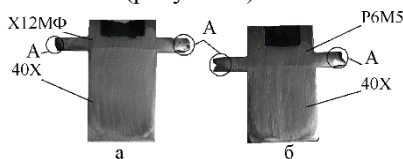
Вид биметаллических образцов полученных скоростным горячим выдавливанием: а) – рабочая часть образца (сталь X12MФ); основа образца (сталь 40X); б) – рабочая часть образца (сталь P6M5); основа образца
